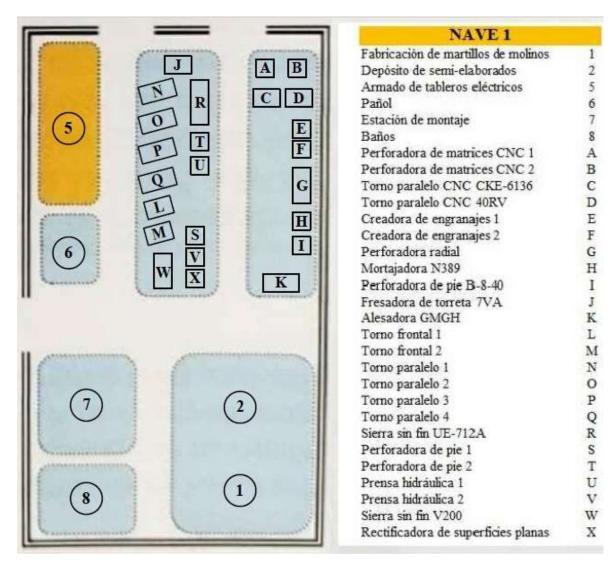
Layout Nave 1 - Planta industrial Giuliani Hnos S.A.
